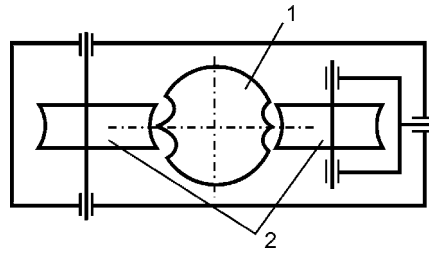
Схема упрочнения режущего инструмента в самоустанавливающемся двухрольковом приспособлении: 1 – упрочняемый инструмент; 2 – ролики
